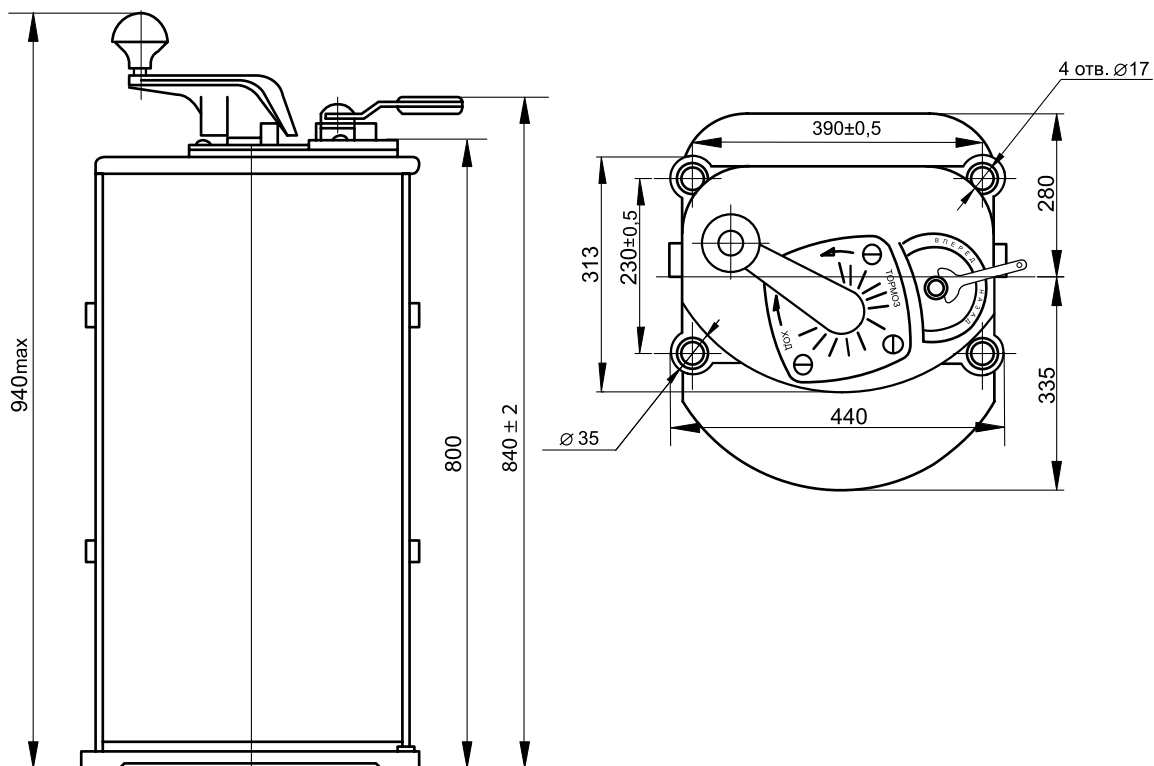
Габаритные и установочные размеры контроллера силового КС –304М
